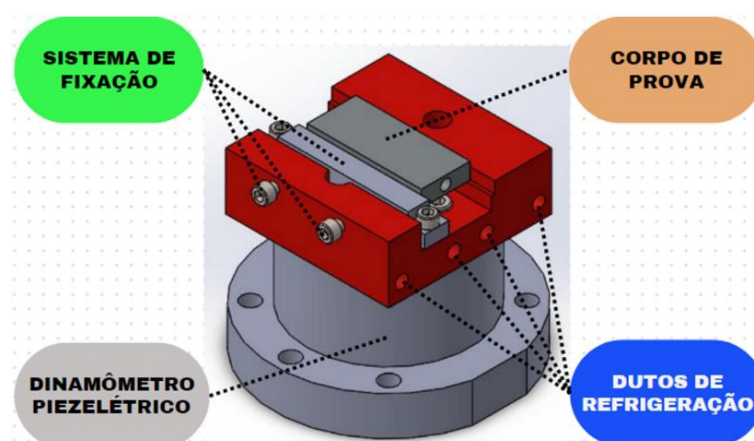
Projeto mecânico do dispositivo de fixação e aquecimento acoplado ao dinamômetro piezométrico.
